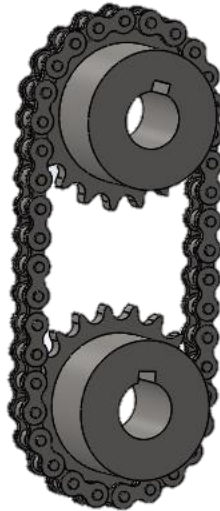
Sistema cadena rodillo a rodillo [Autor].
